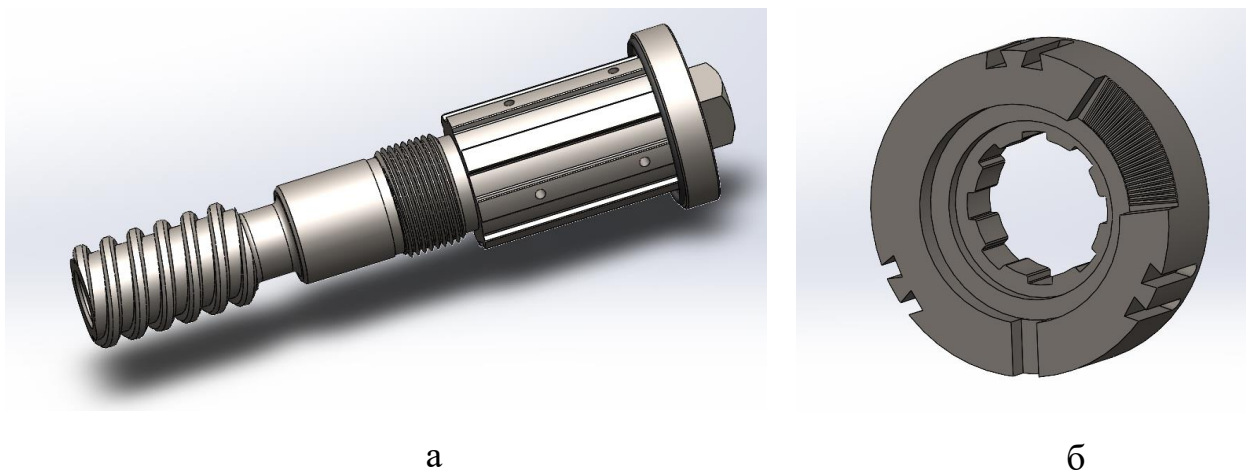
3D-моделі елементів для розрахунку трирізцевої розточувальної головки: а) корпус інструменту; б) перша спеціальна втулка
